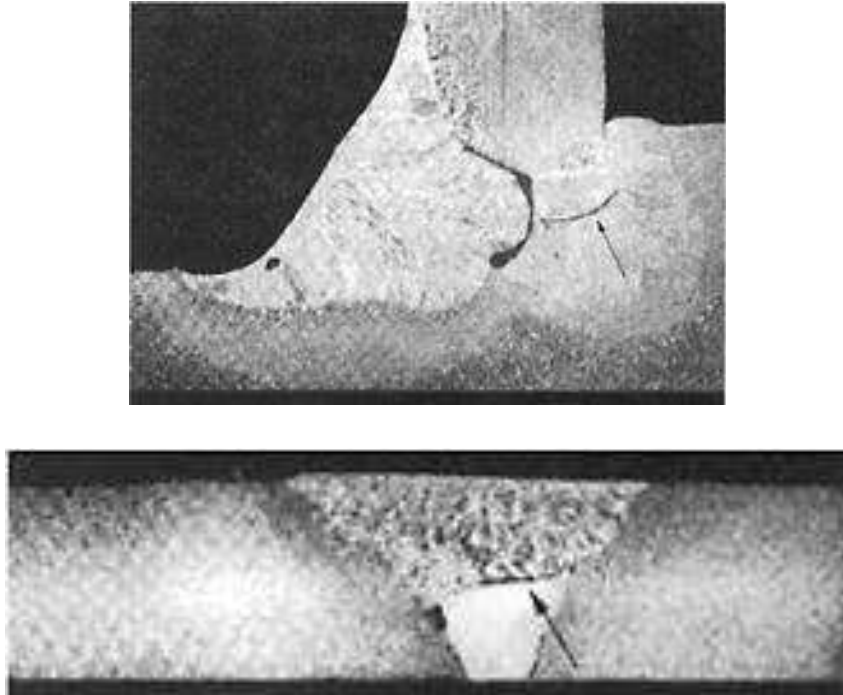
27 *Fisuras alrededor de la ZAC en juntas a tope y en filete.
